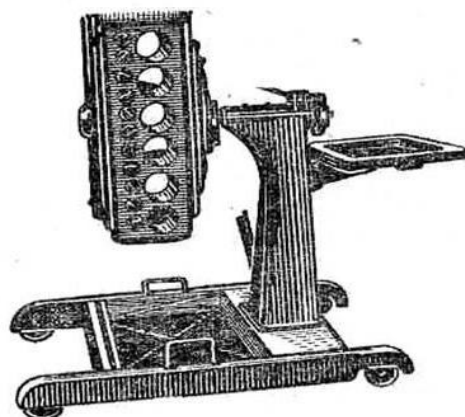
Стенд для ремонту двигунів ОПР-647 [21]
